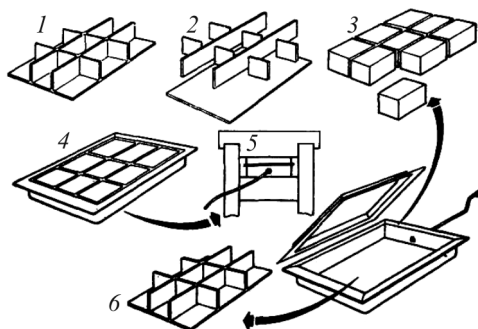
Схема диффузионной сварки крупногабаритной заготовки ребристой панели: 1 – внешний вид панели; 2 – составные элементы; 3 – детали оснастки; 4 – сборка в контейнере; 5 – сварка с использованием открытого прессы; 6 – сваренная заготовка
